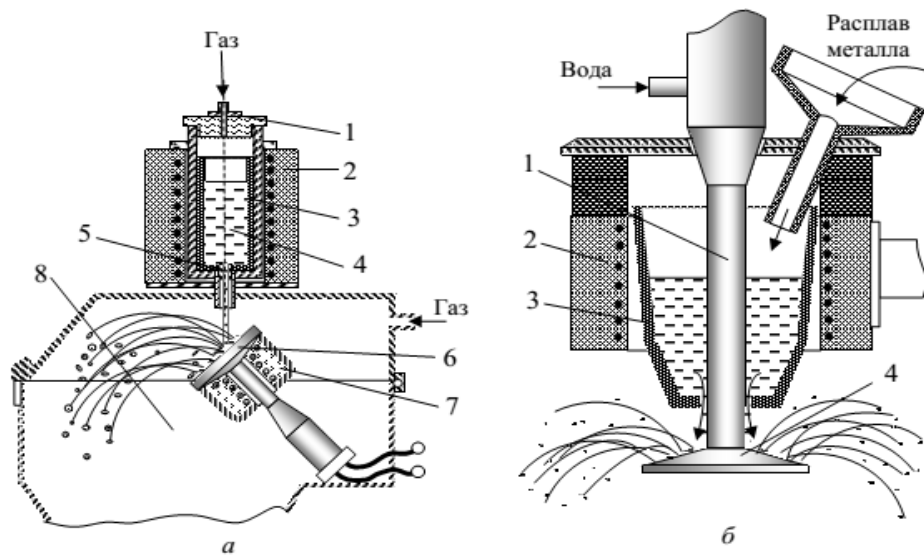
Схемы ультразвукового диспергирования расплавов металлов: а – установка с вынесенным излучателем: 1 – система подачи газа; 2 – печь; 3 – графитовый стакан; 4 – расплав металла; 5 – твердосплавное сопло; 6 – излучатель ультразвуковых колебаний; 7 – нагреватель излучателя; 8 – камера распыления; б – установка с излучателем, проходящим через емкость с расплавом: 1 – концентратор колебаний; 2 – нагревательное устройство; 3 – контейнер с расплавом; 4 – излучатель
